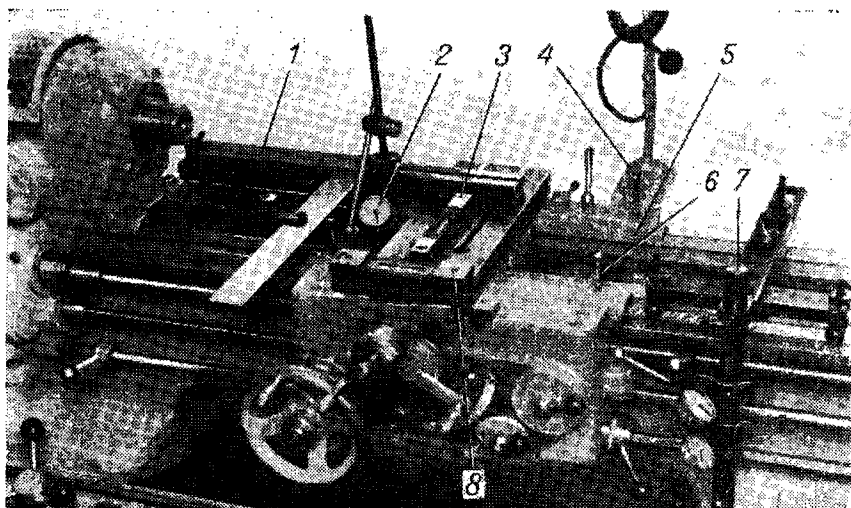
Выверка точности координат каретки суппорта (на примере токарно-винторезного станка модели 1Е61)
